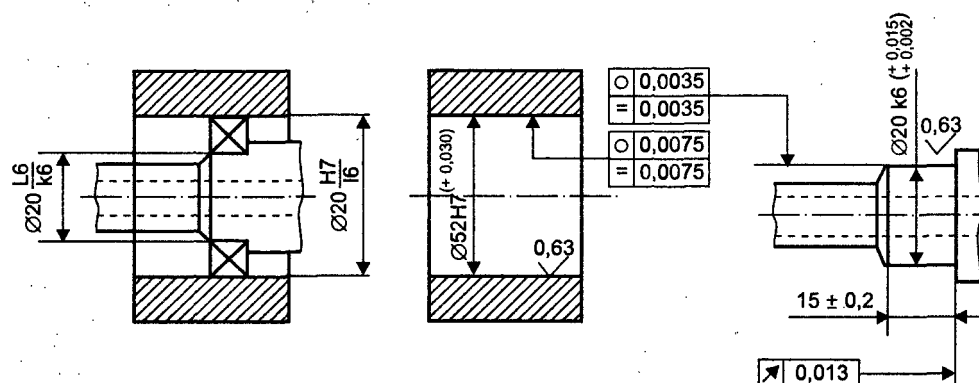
Эскизы подшипникового узла, вала и отверстия
